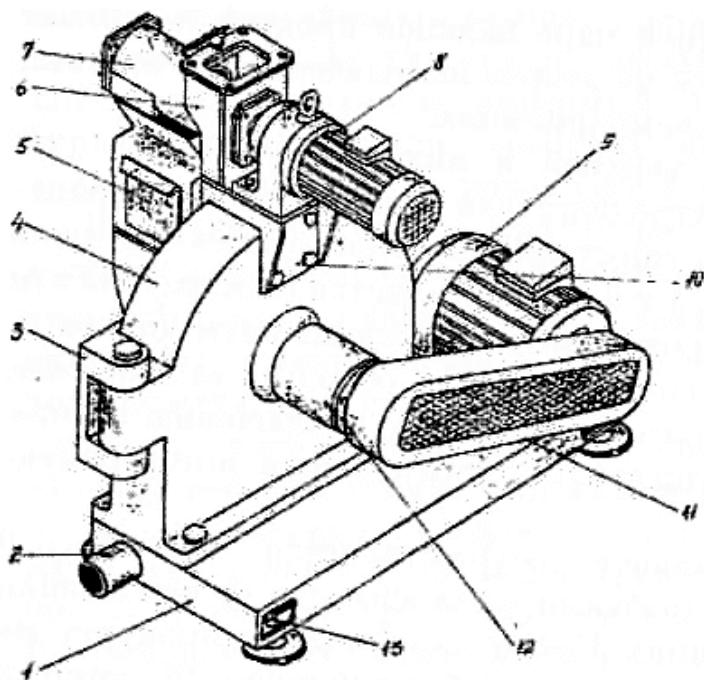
Общий вид центробежного измельчителя ИЦ-1: 1 — сварная рама; 2 — патрубок вывода измельченного продукта; 3 — откидная дверка; 4 — корпус измельчителя; 5 — задвижка; 6 — приемно-распределительное устройство, 7 — шнековый питатель; 8 — мотор-редуктор; 9 — приводной электродвигатель; 10 — установка приемно-распределительного устройства с мотор-редуктором; 11 — ограждение клиноременной передачи; 12 — опора ротора; 13 — виброопора.
